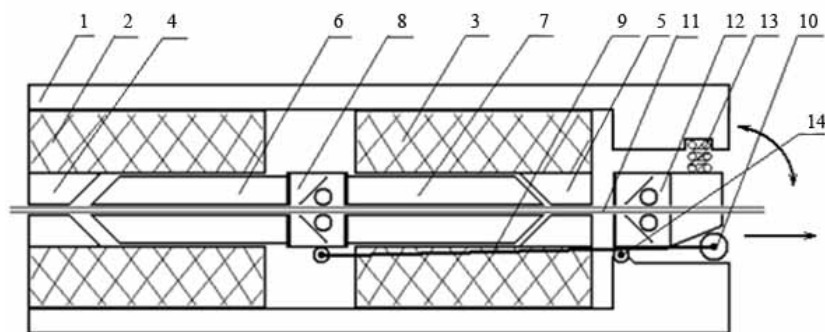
Конструкция импульсного механизма подачи сварочной проволоки.
